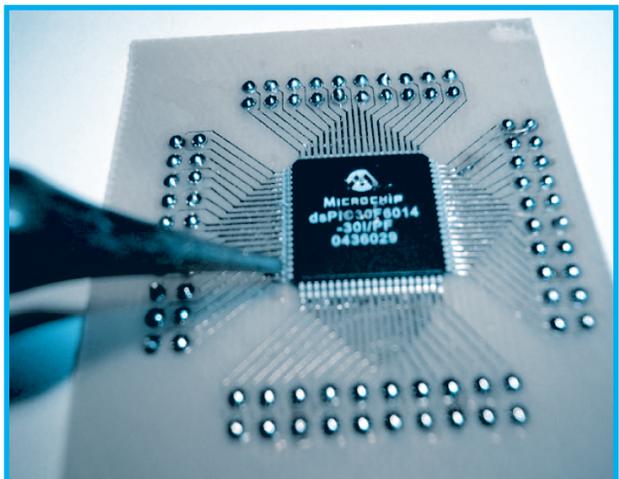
Cuando suelda el componente, asegúrese que el estaño esté brillante, señal que el
